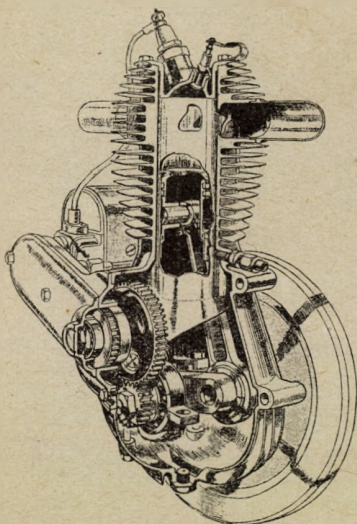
Příčný řez motorem „Barr a Stroud“.
